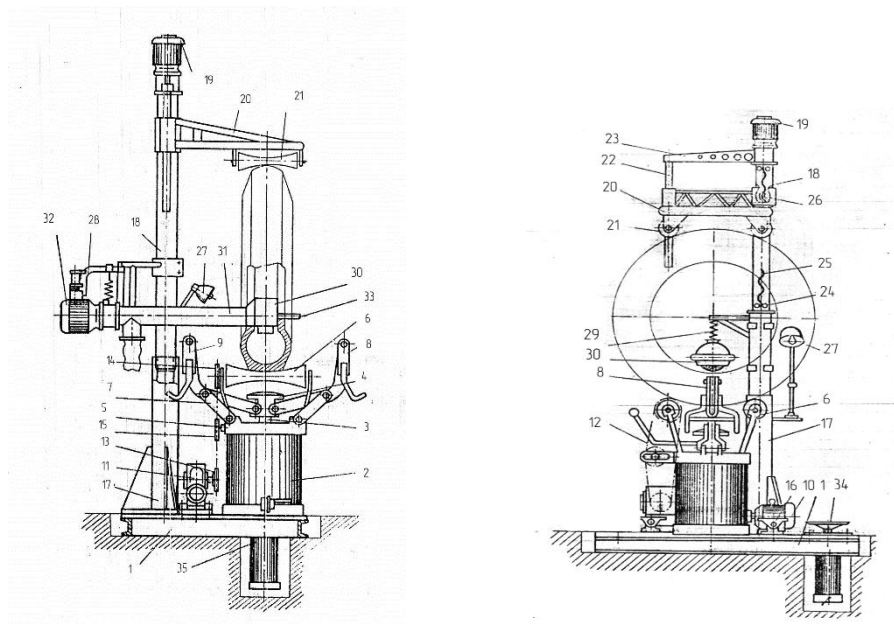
Станок для осмотра, вырезки и шероховки шин:
